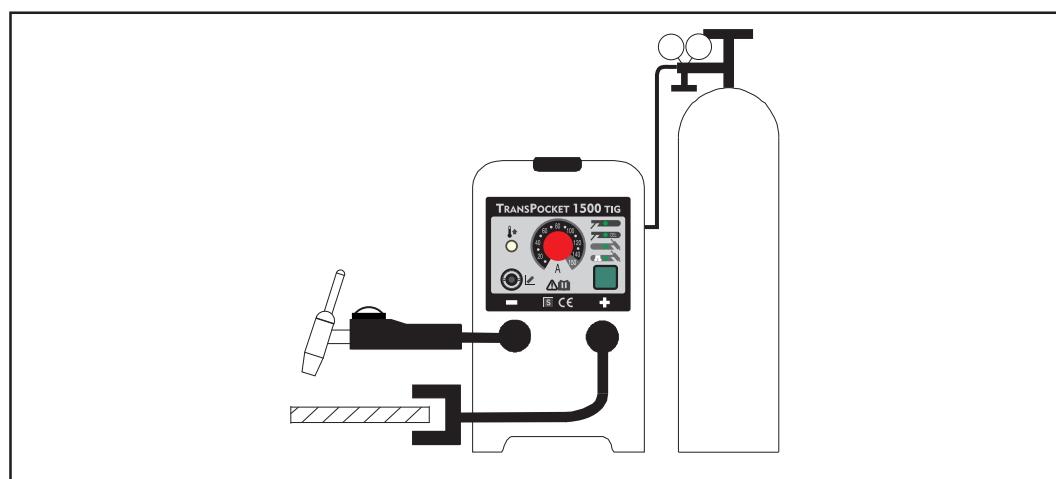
Аппарат TP 1500 с подключенной сварочной горелкой TTG 1600 A.
